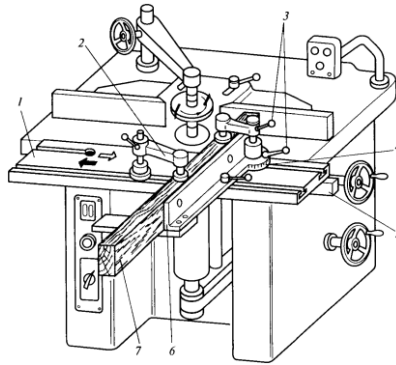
Фрезерний верстат з шипорізною кареткою: 1 – каретка; 2 – пневмопритиск; 3 – стопор; 4 – кругова шкала; 5 – напрямна; 6 – косинець; 7 – заготовка
